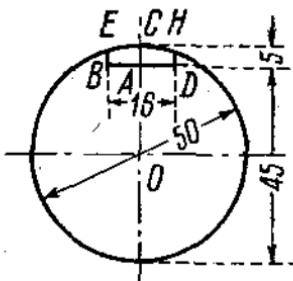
Разметка профиля шпоночного паза на торце вала.
